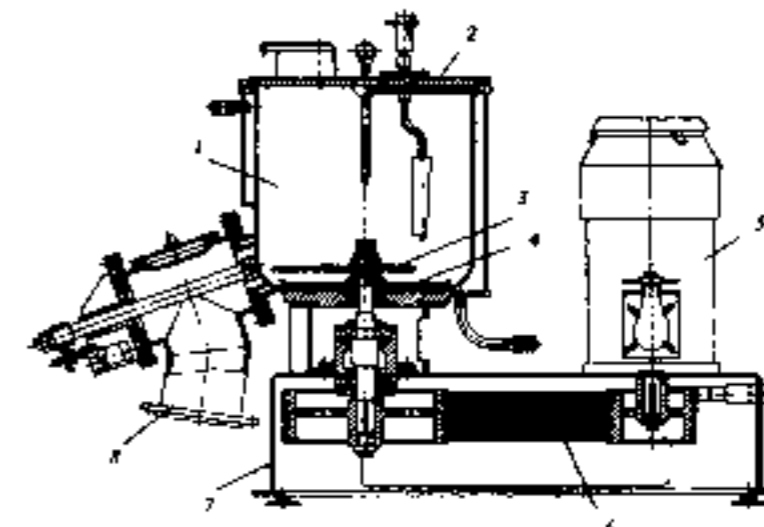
Центробежный лопастной смеситель типа ЦЛ
